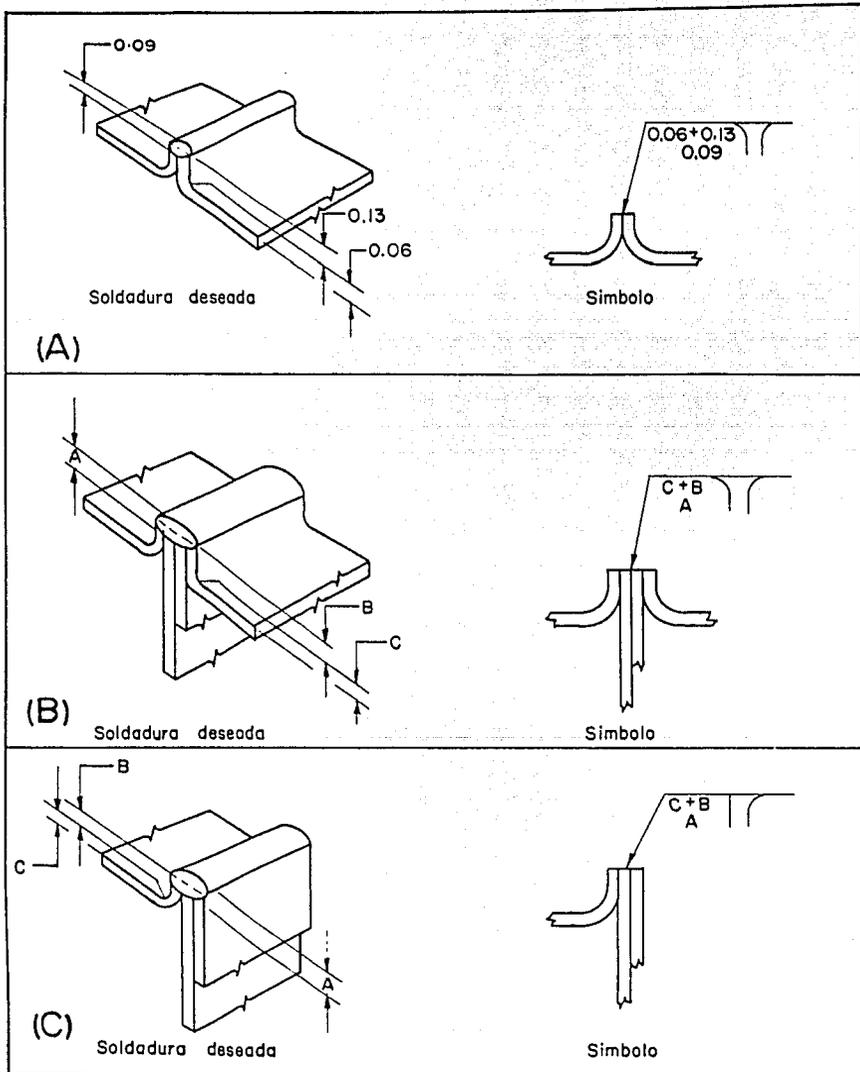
Aplicación de los símbolos de soldadura en el borde y en la esquina del ala
